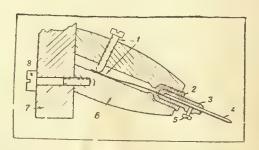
Способ крепления якоря в адаптере т. Федорова: 1—струна, держащая якорь, и винт крепления струны; 2—резина; 3—якорь; 4—игла; 5—винт крепления иглы; 6—тело магнитопровода; 7—полюс магнита; 8—винт крепления детали 6
